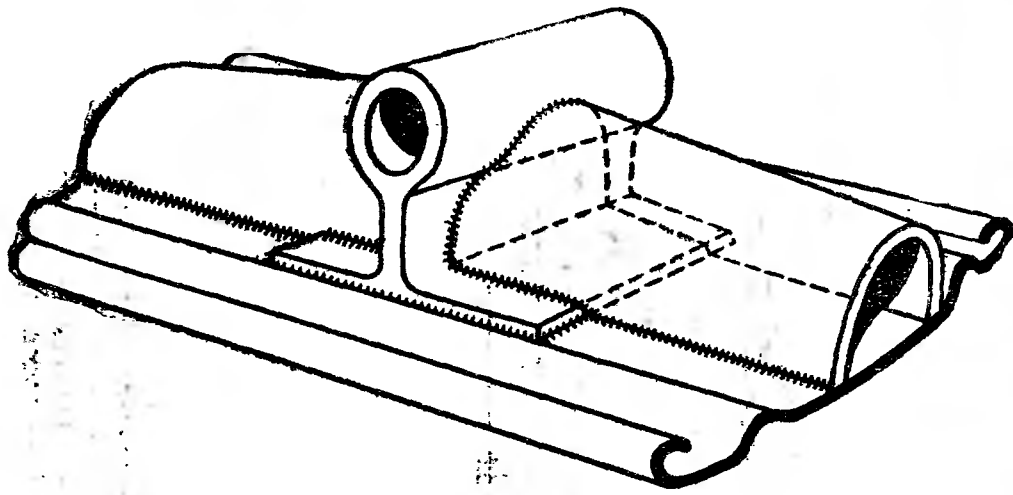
Полуужесткая сварная лыжа — разрез и участок установки кабанчика.
